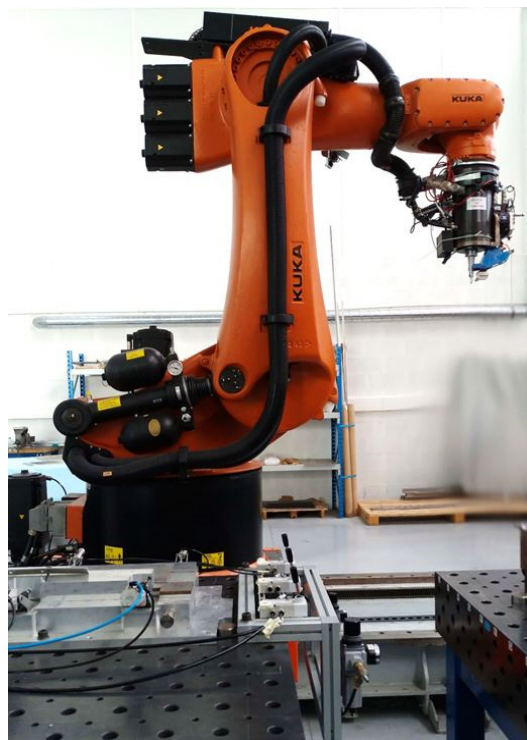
Robot articulé utilisé pour le soudage de l'ensemble des tôles.
